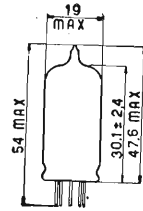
Dimensioni di ingombro della valvola 1A3.
